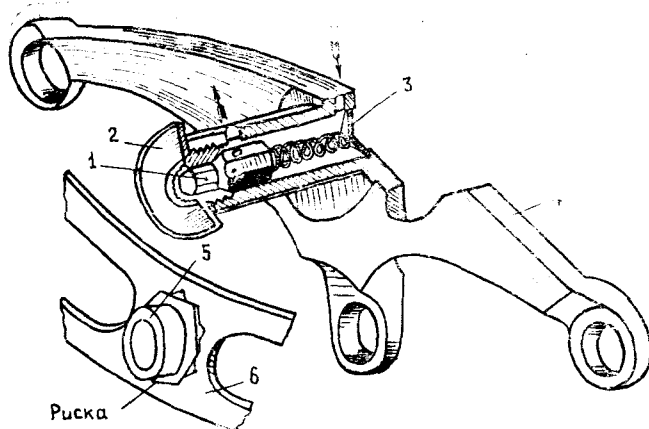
Ось двойной шестерни: 1—замок; 2—пробка; 3—заглушка; 4—фланец; 5—эксцентриковая втулка; 6—стопорная планка
